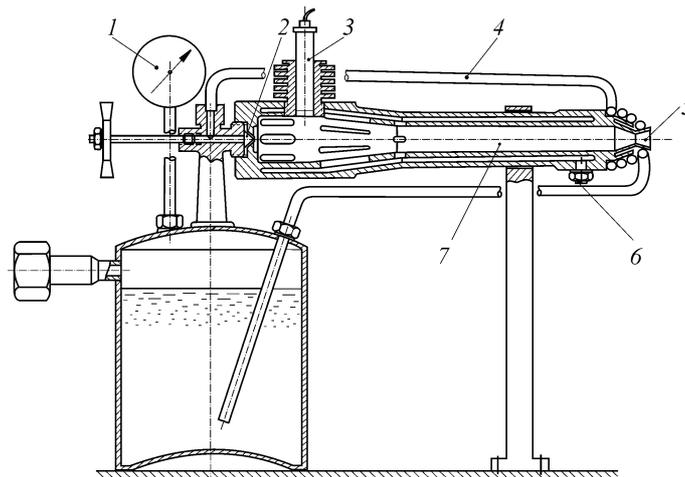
Схема двигателя ОР-1: 1 — манометр, 2 — форсунка для подачи бензина, 3 — свеча зажигания, 4 — трубка охлаждения, 5 — сопло, 6 — штуцер для подвода сжатого воздуха, 7 — камера сгорания.
